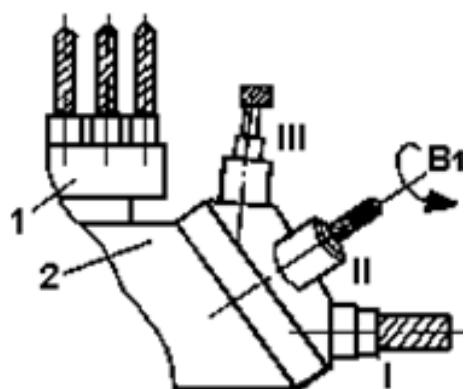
Схема компоновки верстата револьверною головкою
